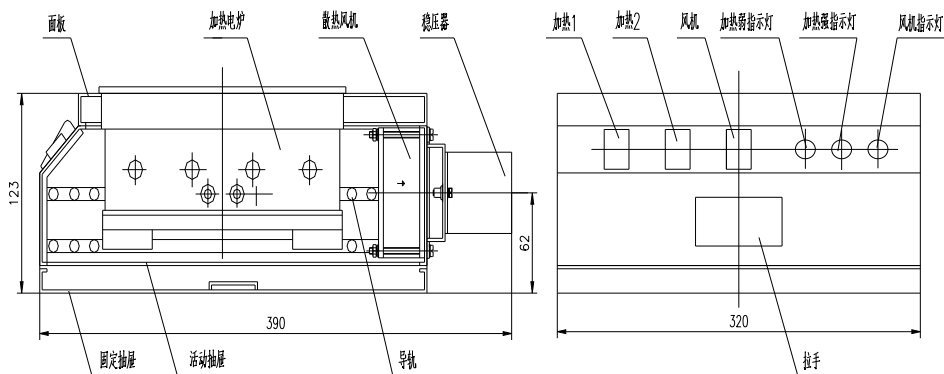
Схема конструкции электронагревателя типа WRFR-1
